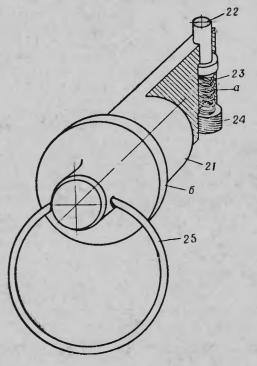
Палец кропштейна казениика: 21 - палец; 22 - стопор; 23 - пружина: 24 - винт; 25 - разводное кольцо; a - гнездо для стопора; 6 - упорный бурт
